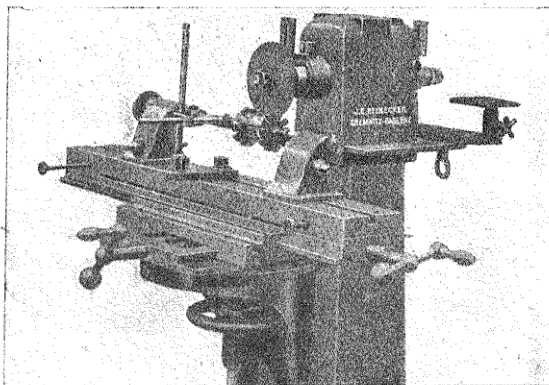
Affûtage d'une fraise de forme sur machine Reinecker.
